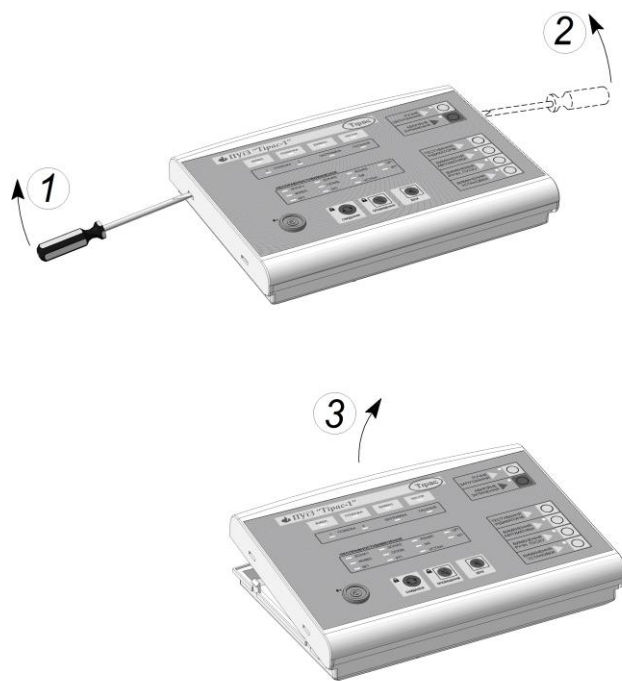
Порядок відкриття корпусу ПУіЗ
